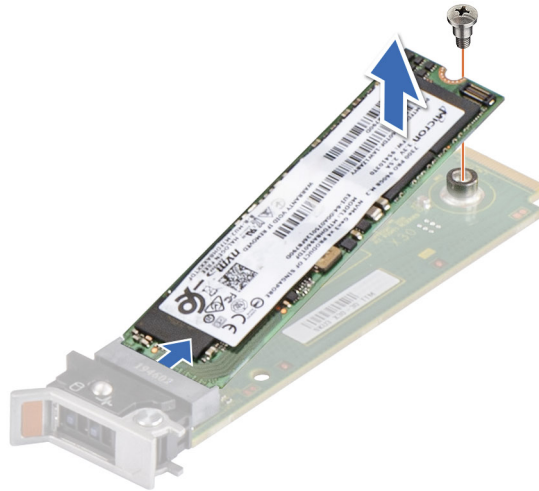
Entfernen des M.2-SSD-Laufwerks
